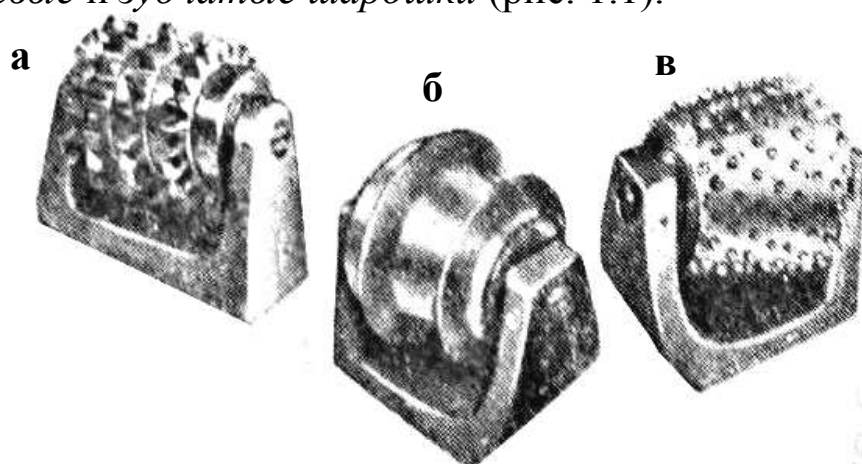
Шарошки фирмы «Хугес Тул» США: а – трехвенцовая зубчатая; б – двухдисковая; в – многовенцовая штыревая
